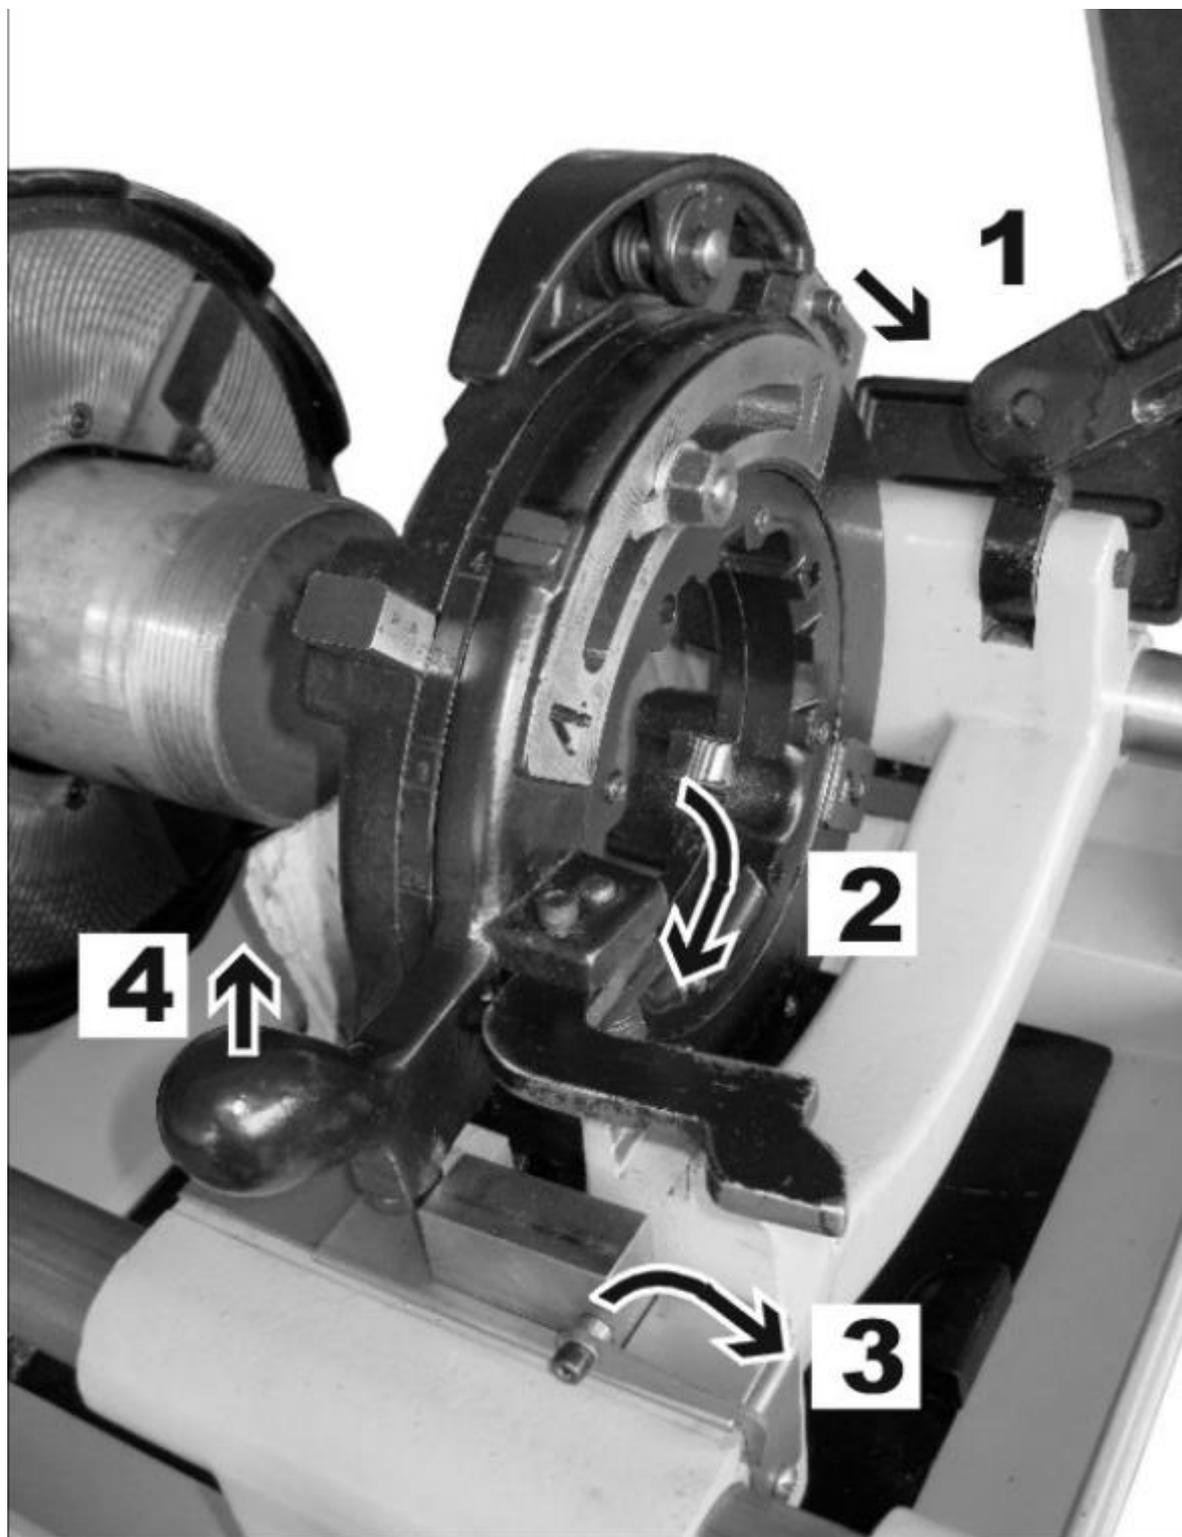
Установка 2 1/2"-4" резьбонарезной головки для NPSM или BSPP резьбы
